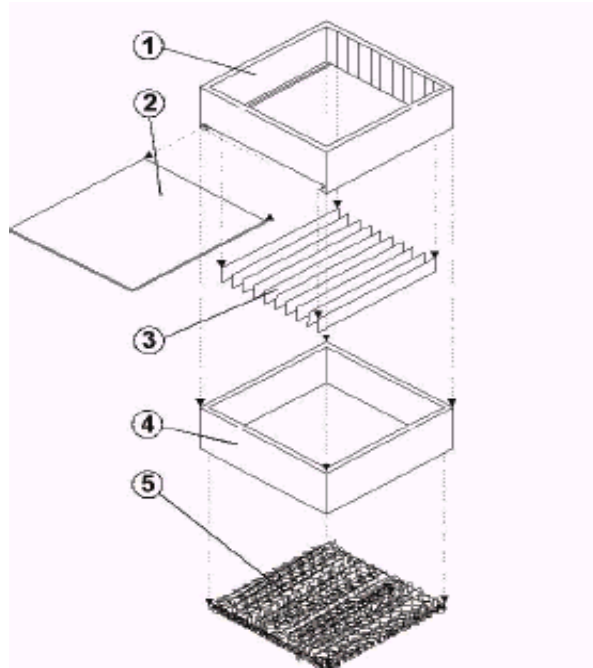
Sistema composto por tela metálica para facilitar a orientação das partículas de madeira.
